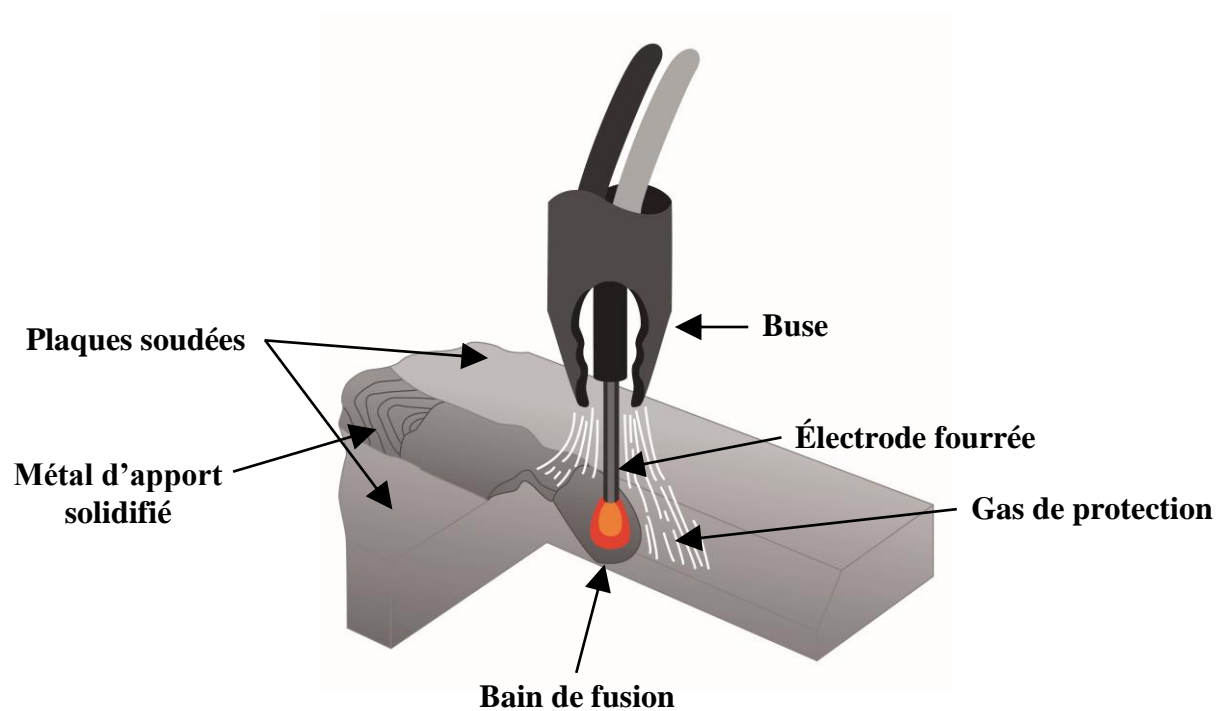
Illustration du procédé de soudage à l'arc avec fil fourré.
